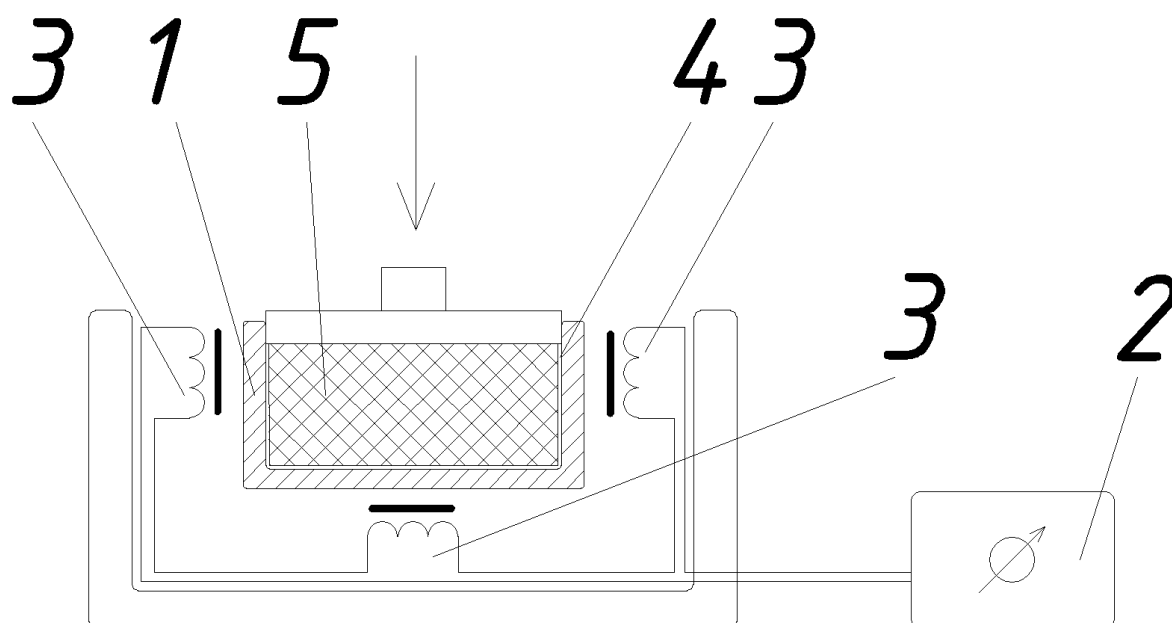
Схема установки для упрочнения полимерных деталей в процессе их изготовления.
